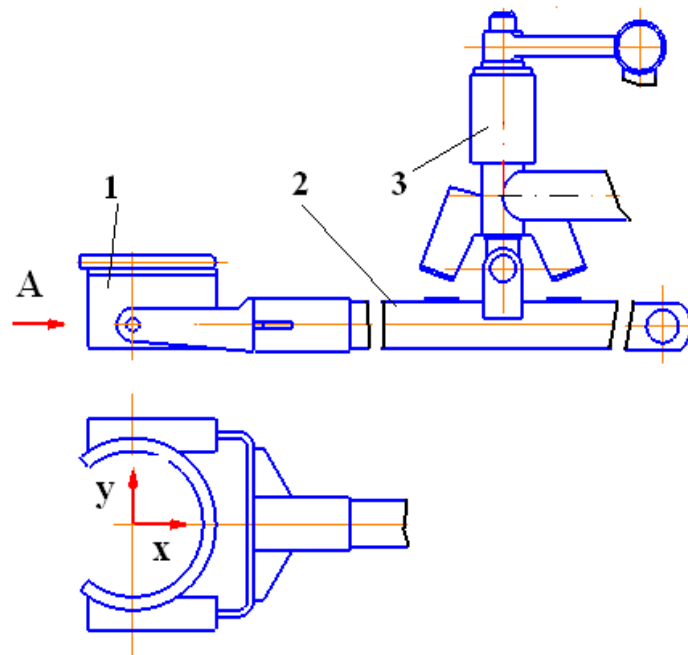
Захват манипулятора для защиты струи металла при разливке на МНЛЗ: 1 – захват манипулятора; 2 – стрела манипулятора; 3 – опорный узел
